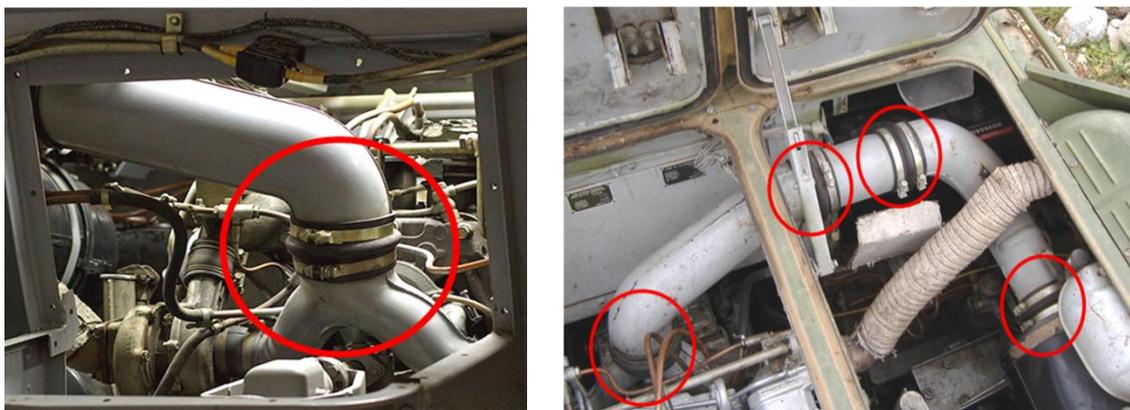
Патрубки и соединительные шланги системы питания двигателя воздухом
